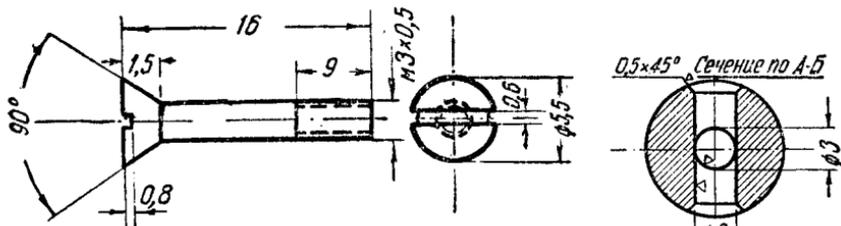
Дет. № 325. Винт крепления рычага к поплавку
